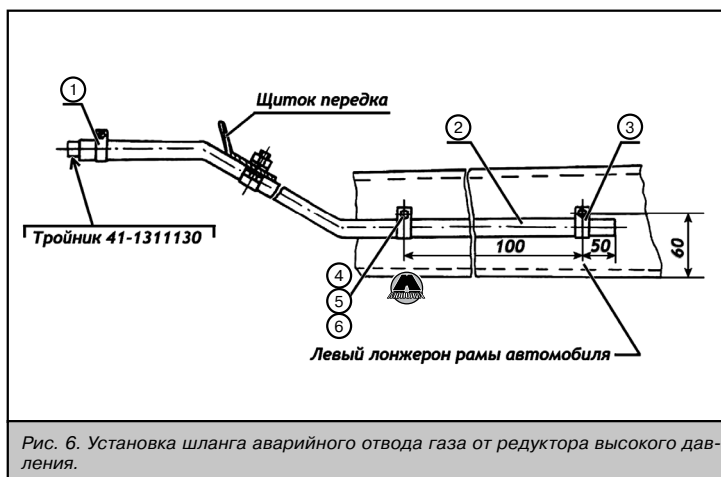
Установка шланга аварийного отвода газа от редуктора высокого давления.
